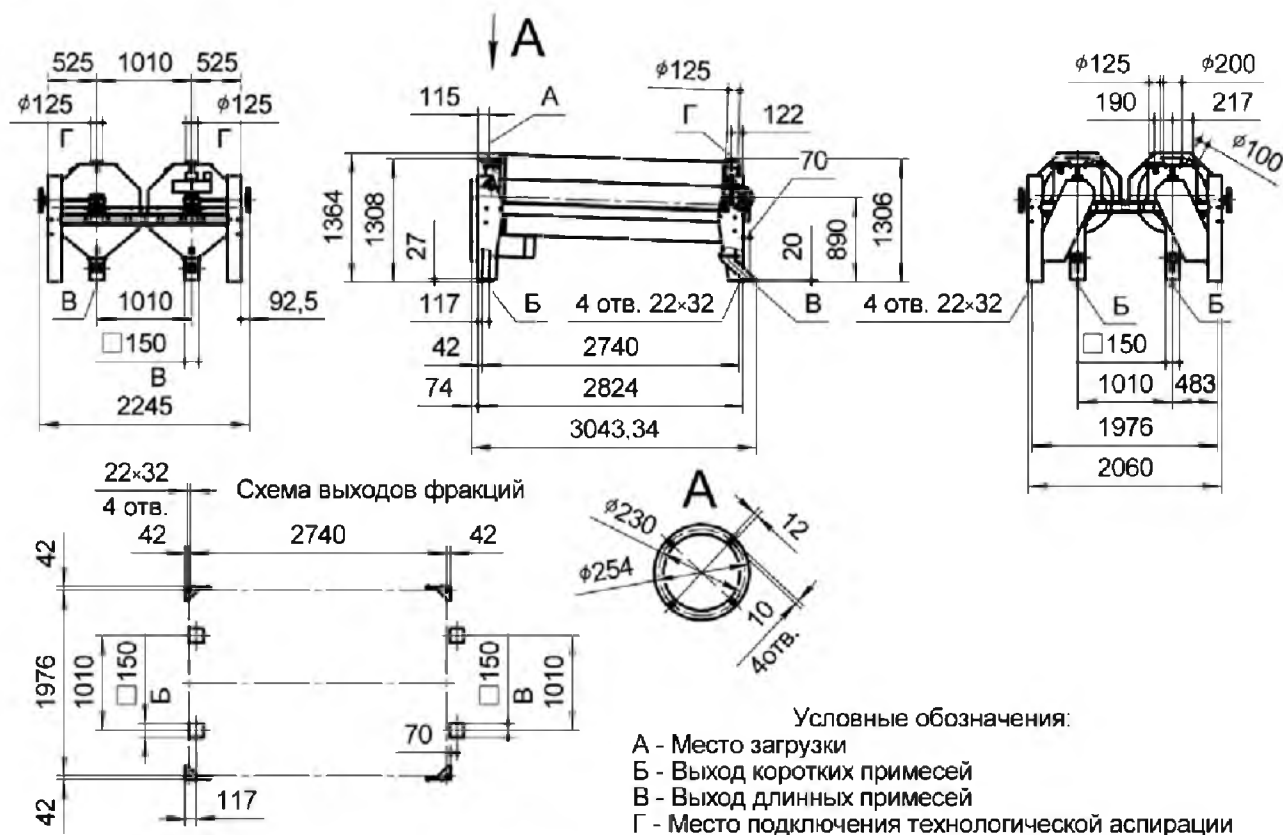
Установочные и присоединительные размеры блоков триеров БК-800-16 и БО-800-16.
